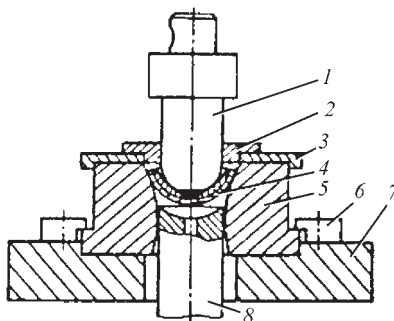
Типовая конструкция штампа для вытяжки заготовок в матрице с криволинейным профилем:
